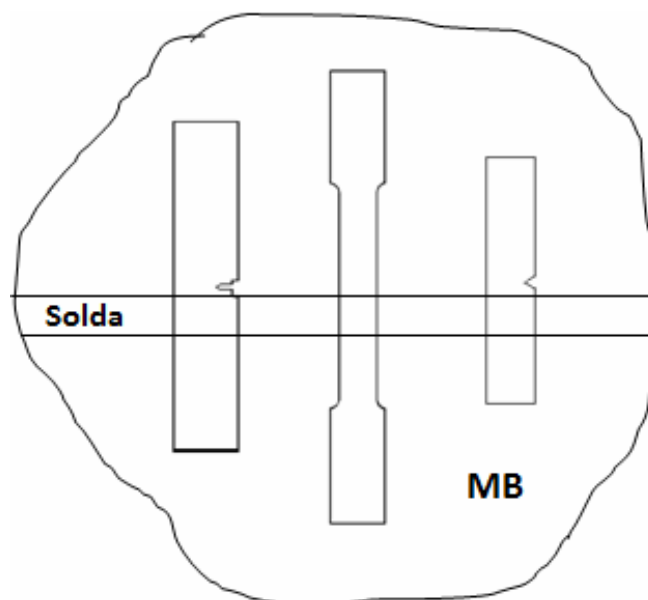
Posição de retirada de corpos de prova de CTOD, tração e Charpy, respectivamente, a partir da peça soldada, onde MB é o metal de base (chapa de aproximadamente 6,5 mm).
